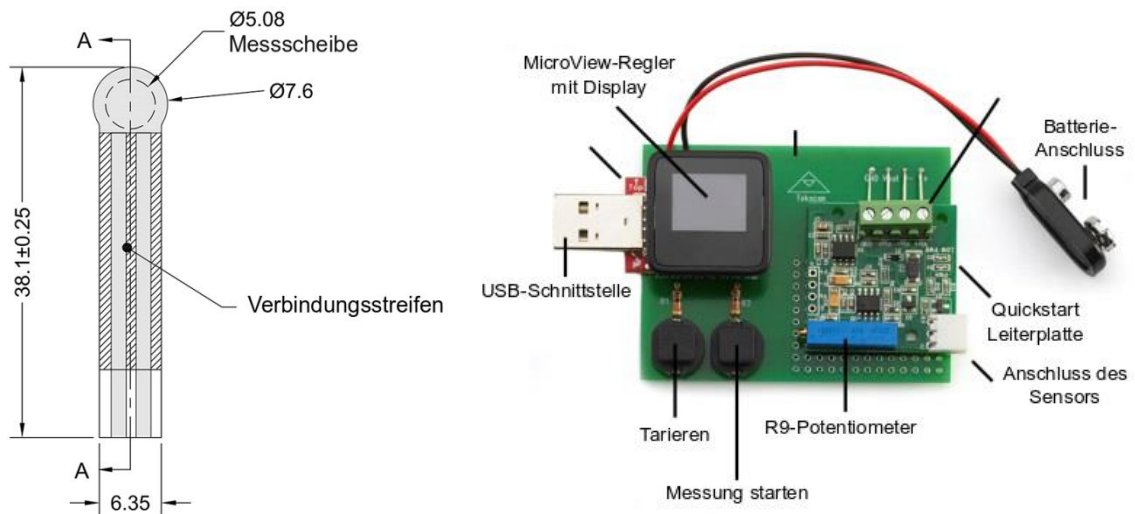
Aufbau des Flexkraftsensors (links) und dessen Plattform (rechts)
